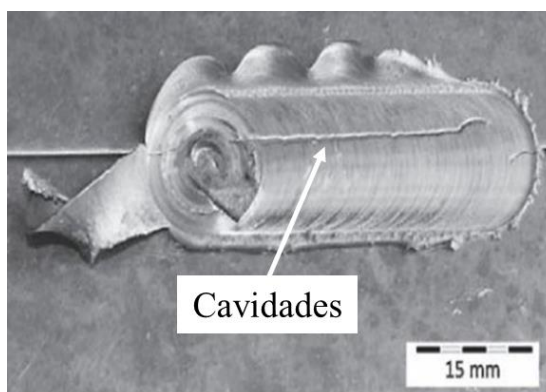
Defeito de cavidade obtida numa soldadura dissimilar entre a AA5083 e AA2017 [96].
